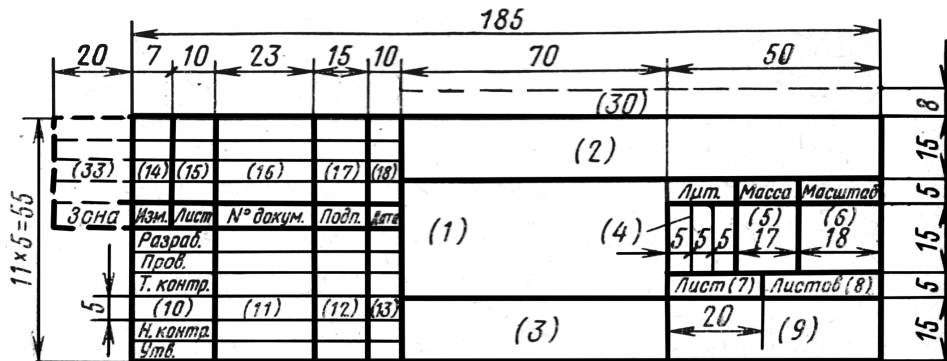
Основний напис для креслень і схем форма 1 за ГОСТ-2.104.95
